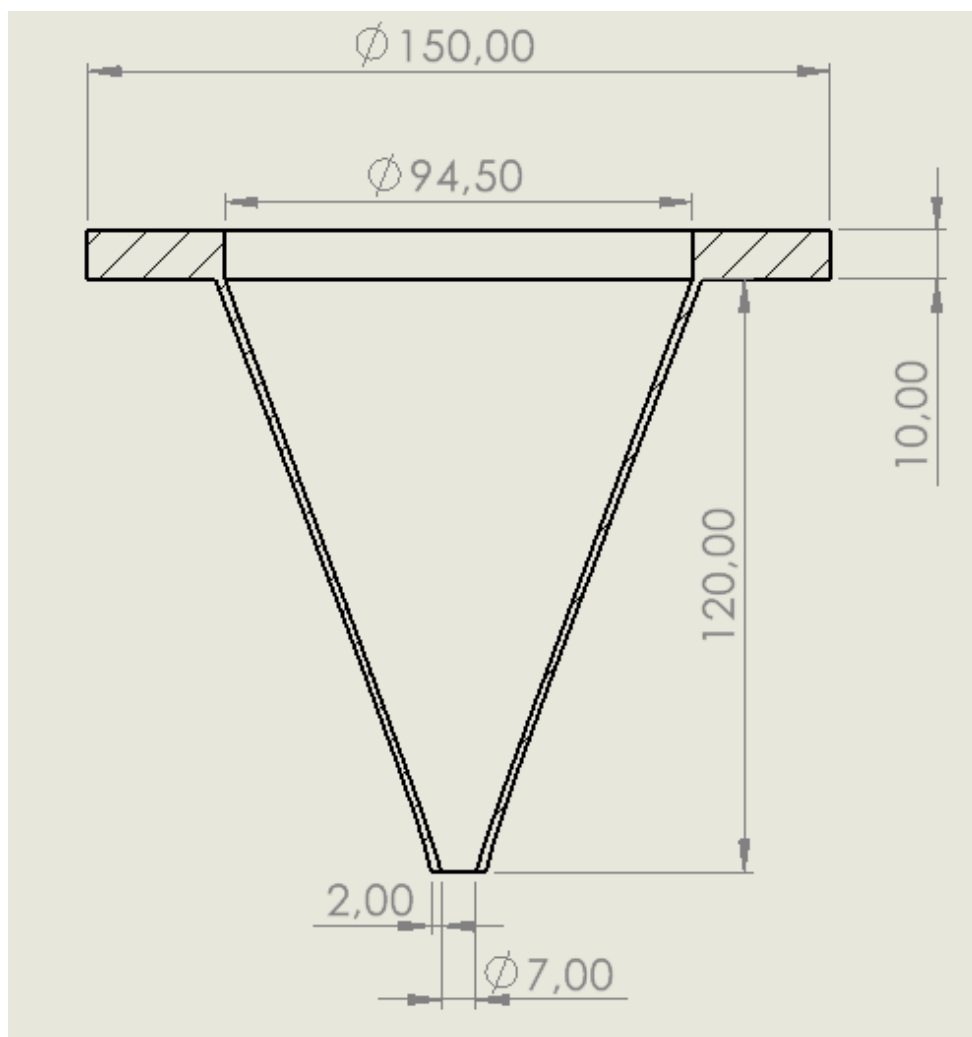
disegno tecnico quotato dell'imbuto di raccolta
